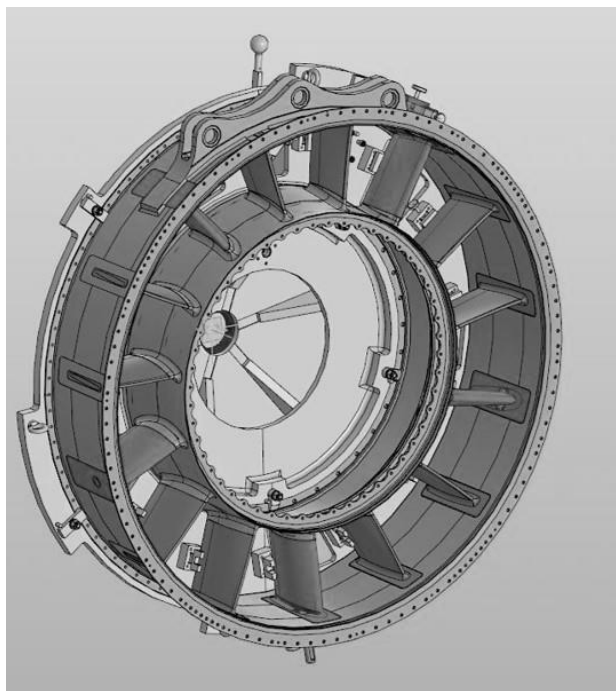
Сборочно-сварочное приспособление без прижимов
